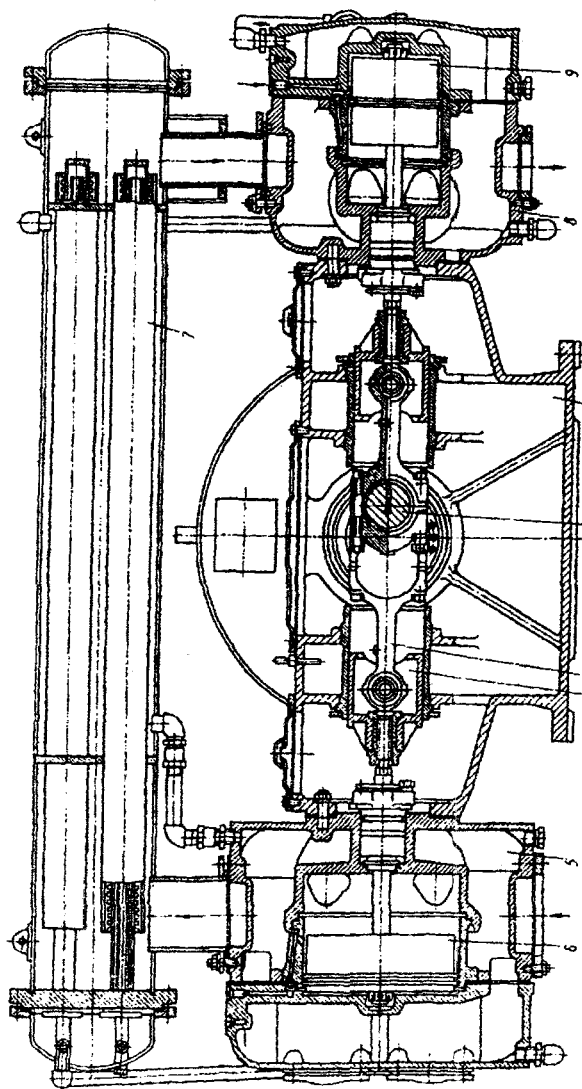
Горизонтальный оппозитный поршневой компрессор:
